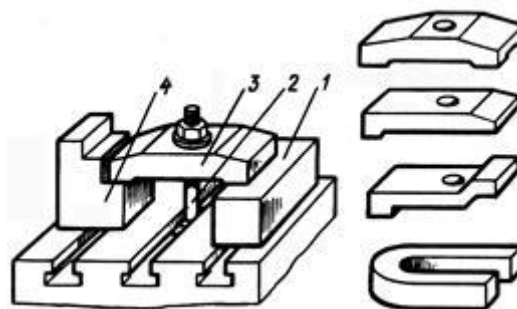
Прихвати для закріплення заготовок на фрезерному верстаті
